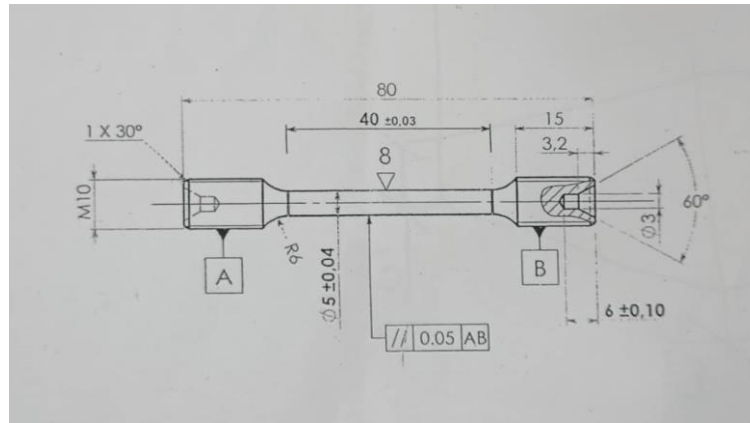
Dessin définition de l'éprouvette de la machine numérique.
